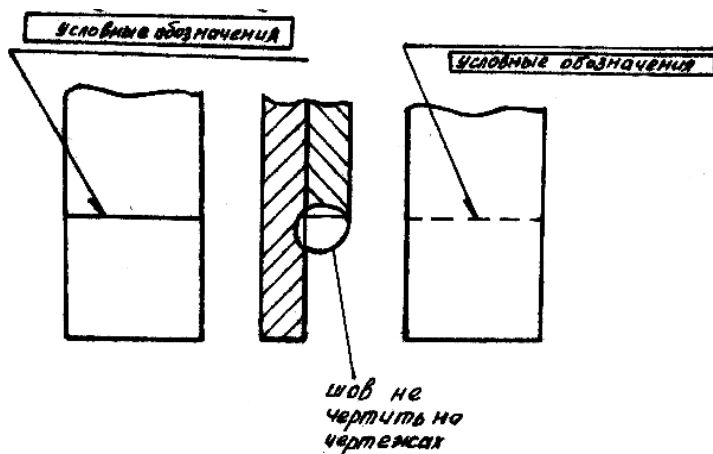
Изображение сварных швов на чертежах
